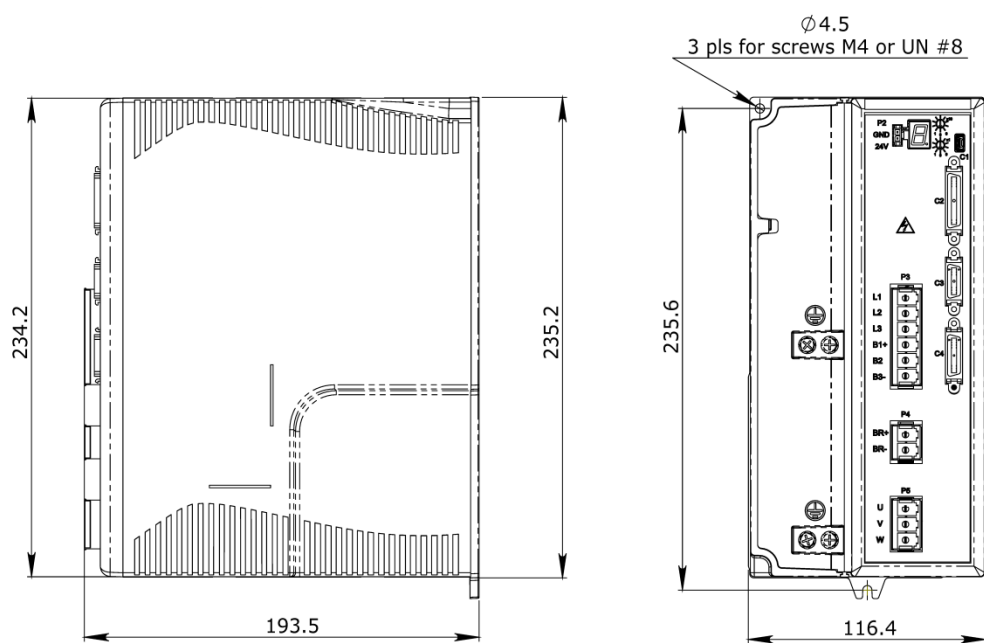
CDHD-012 (400/480 VAC) - 尺寸 (mm)
